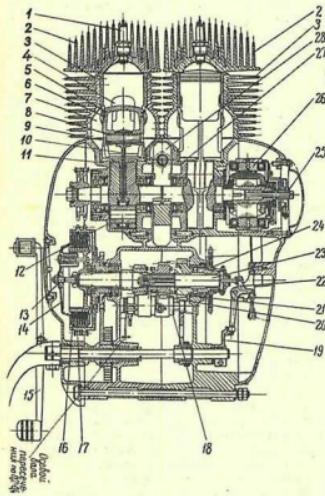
Двигатель с коробкой передач в разрезе: 1 — свеча зажигания; 2 — головка цилиндра; 3 — цилиндр; 4 — выпускное окно; 5 — поршень; 6 — поршневое кольцо; 7 — перепускной канал; 8 — поршневая палец; 9 — втулка верхней головки шатуна; 10 — шатун; 11 — крышка кривошипной камеры; 12 — палец кривошипа; 13 — регулировочный винт сцепления; 14 — нажимной диск сцепления; 15 — педаль переключения передач; 16 — диски сцепления; 17 — наружный барабан сцепления; 18 — вал переключения передач; 19 — кулачок автомата сцепления; 20, 21 — шестерни коробки передач; 22 — рычаг выжимки сцепления; 23 — ведущий вал; 24 — ведомый вал; 25 — кулачок прерывателя; 26 — генератор; 27 — крышка кривошипной камеры; 28 — ма-ховик.
